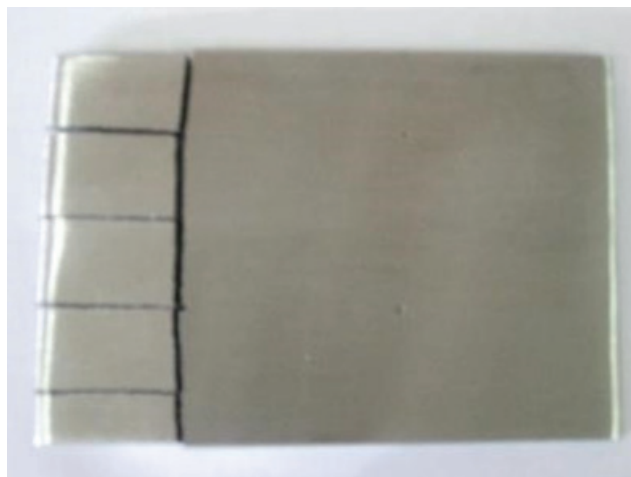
Внешний вид образца лопатки 1, упрочненного СВЧ, 0,3
